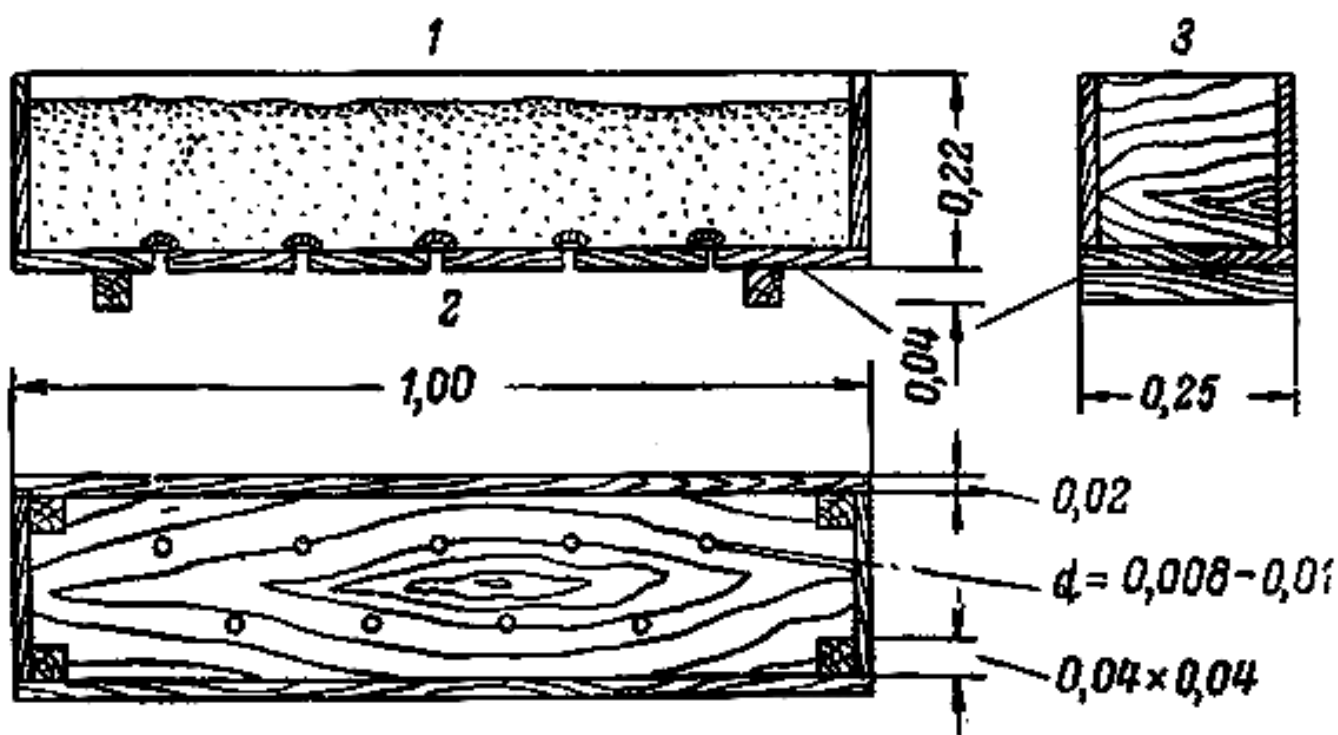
Простой цветочный ящик (размеры в метрах): 1 — продольный разрез; 2 — вид сверху; 3 — торец
